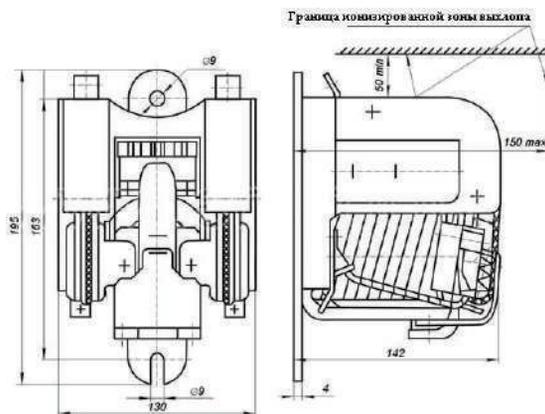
Габаритные, установочные размеры КЖД-121 Y2
